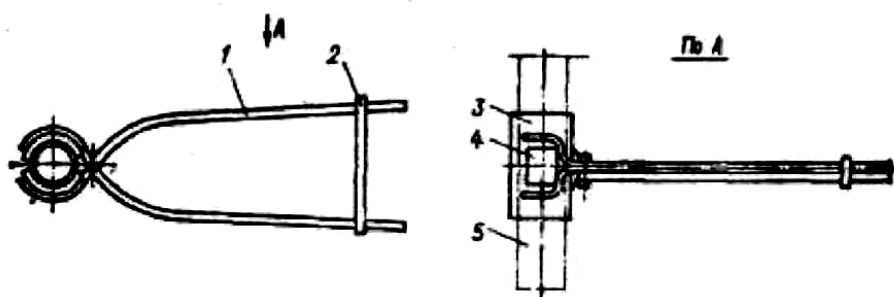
Клещи для центровки труб: *1* – рукоятка; *2* – хомут стопорный; *3* – накладка; *4* – окно для прихватки; *5* – стыкуемые трубы
